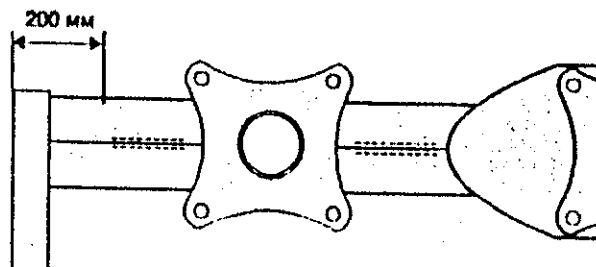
Контроль сварного шва нижней стенки продольной балки рамы
